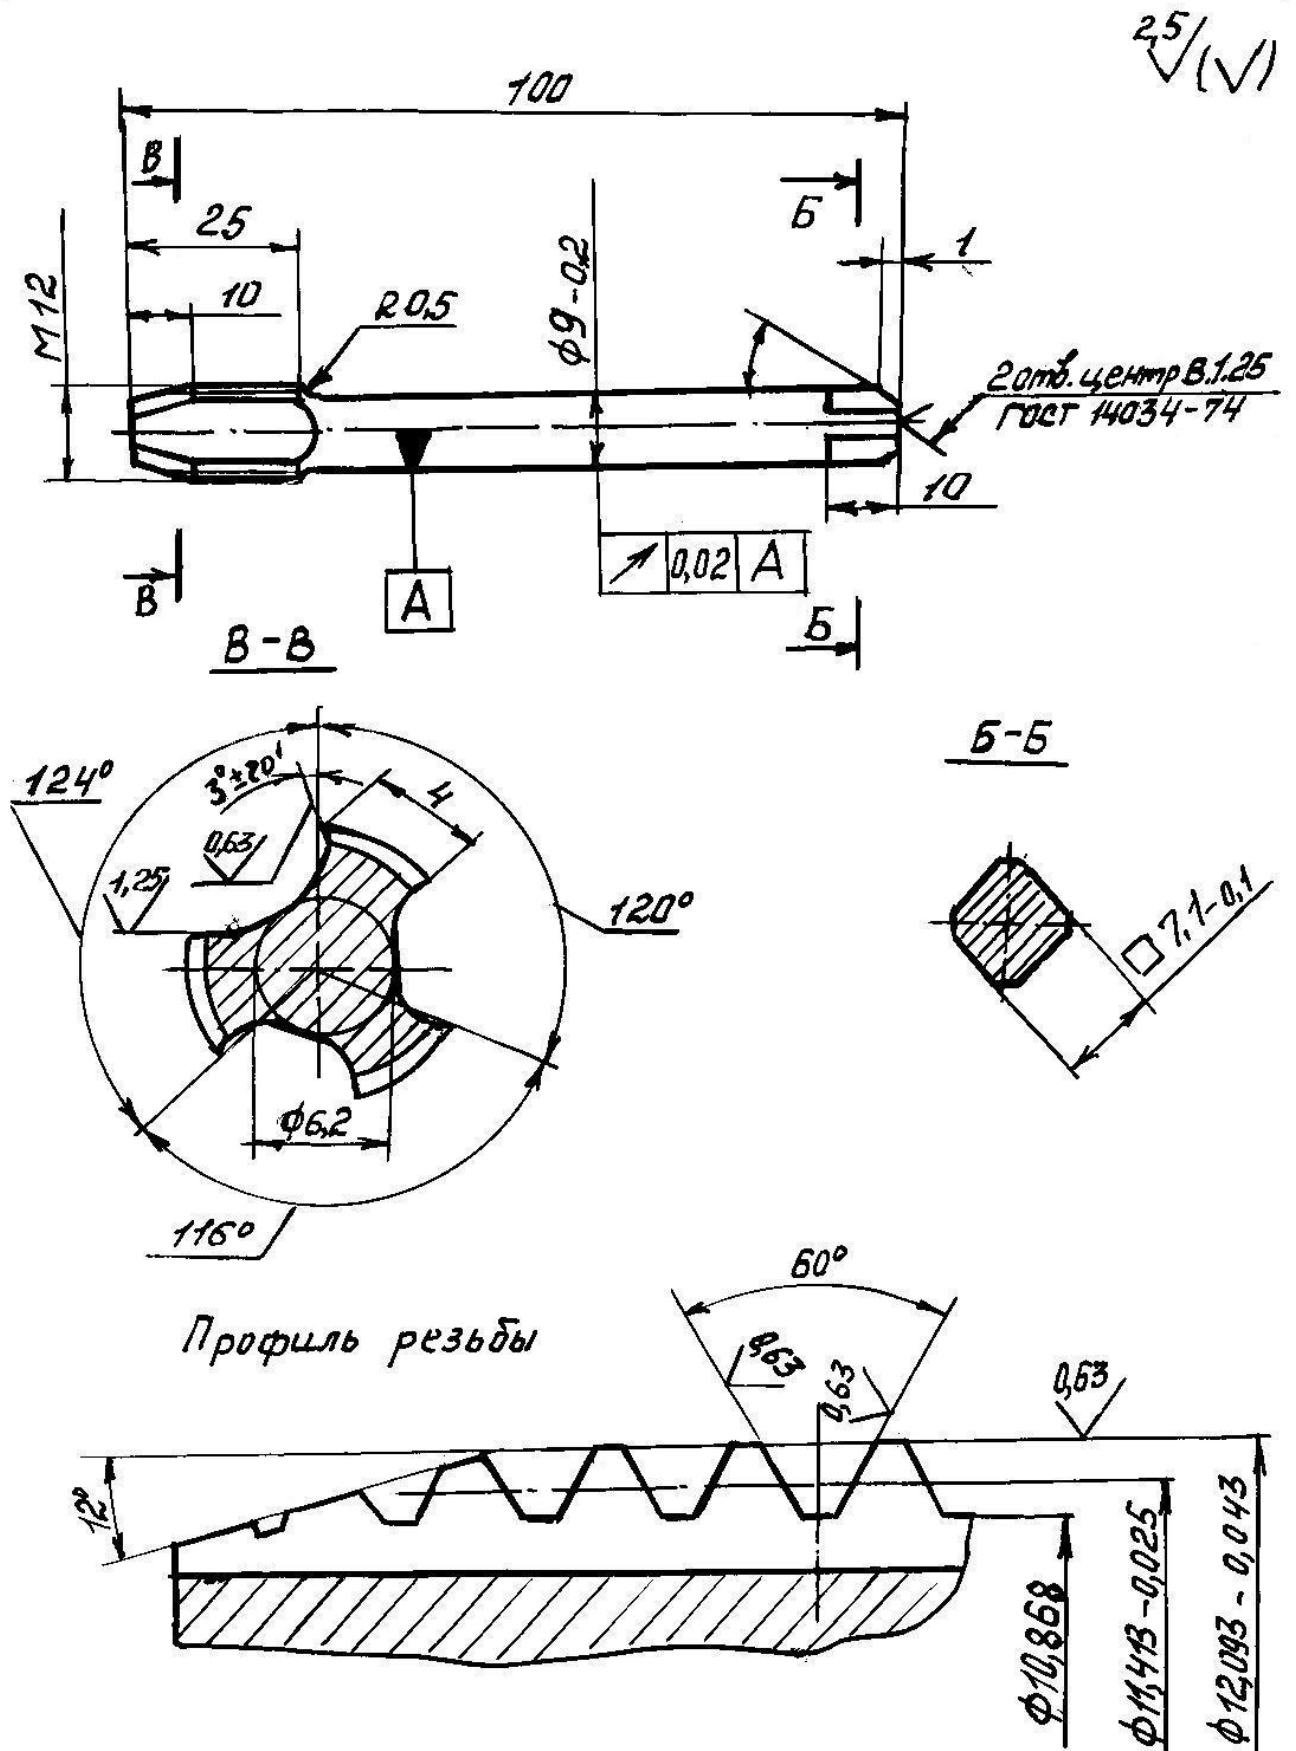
Метчик с неравномерным расположением режущих зубьев
